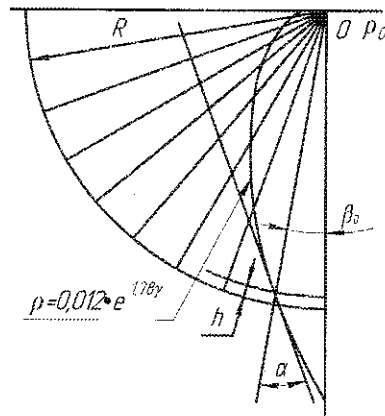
Построение профиля рабочей поверхности пластинчатого выталкивателя.
